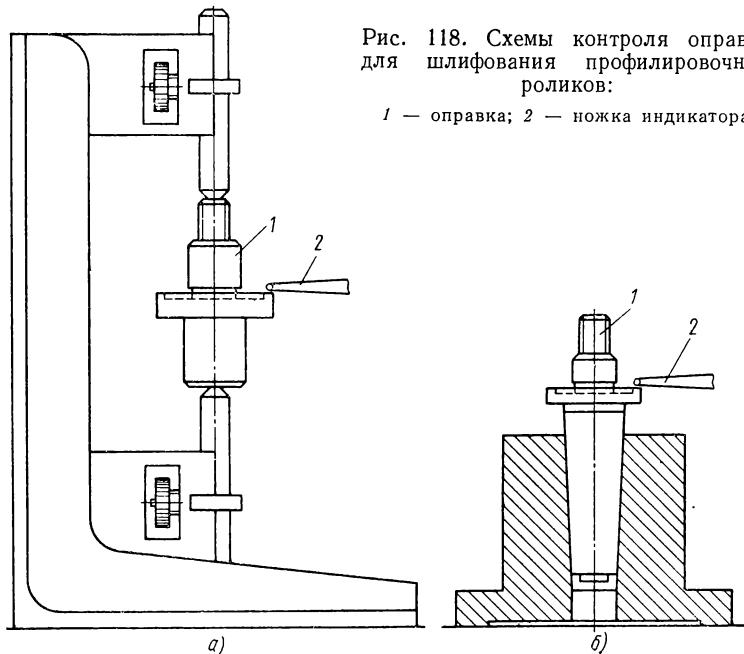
Схемы контроля оправок для шлифования профилировочных роликов:
